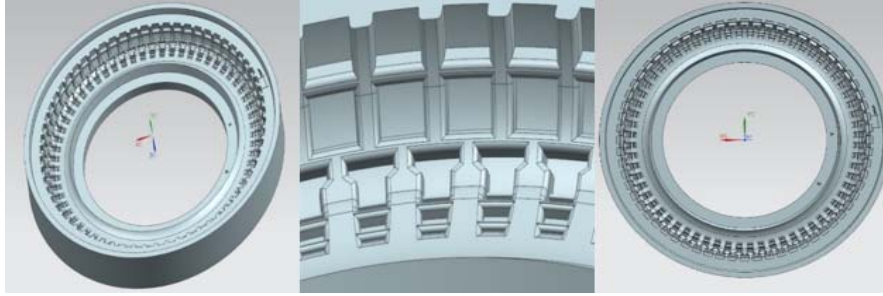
CAD/CAM çizimi (CAD / CAM drawing)
